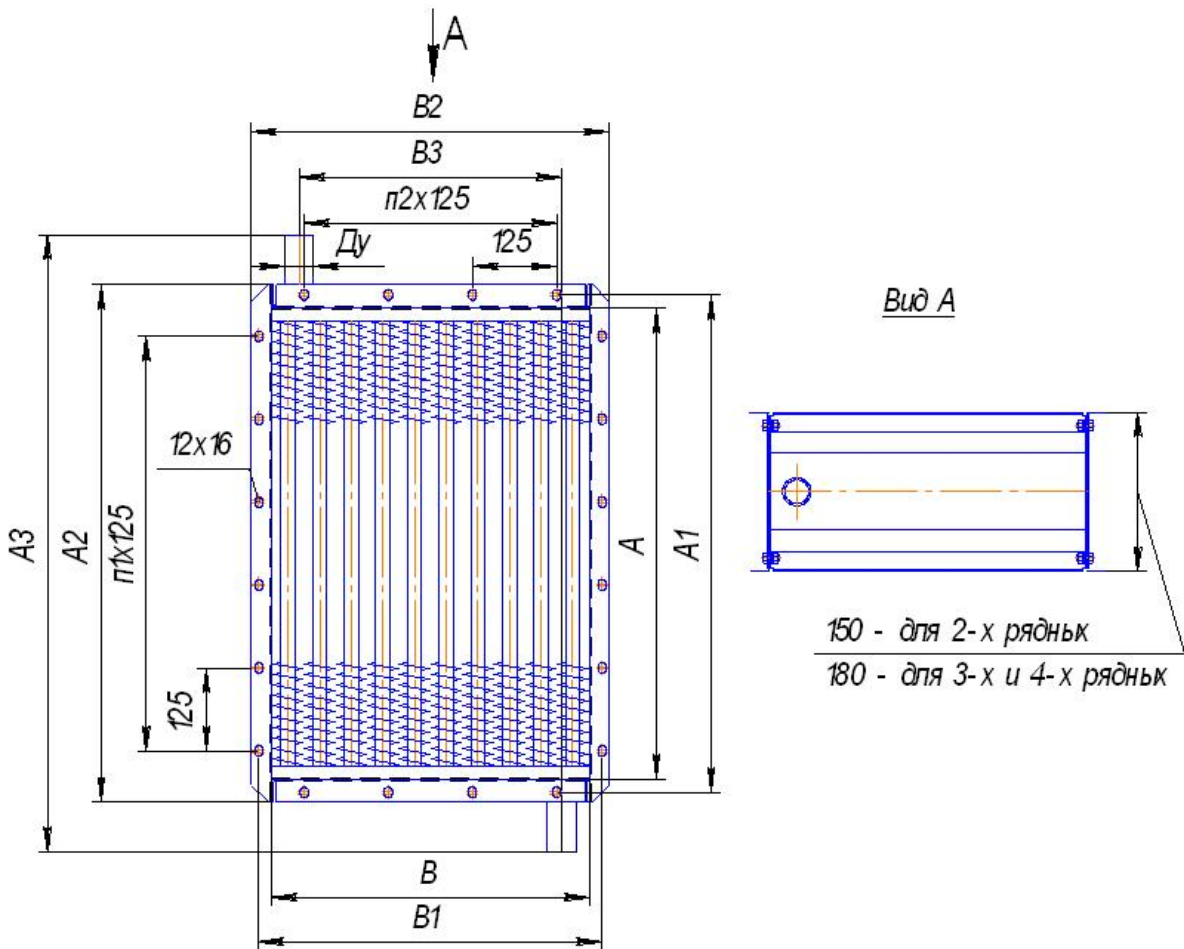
Конструктивные размеры калориферов КФС, КФБ
